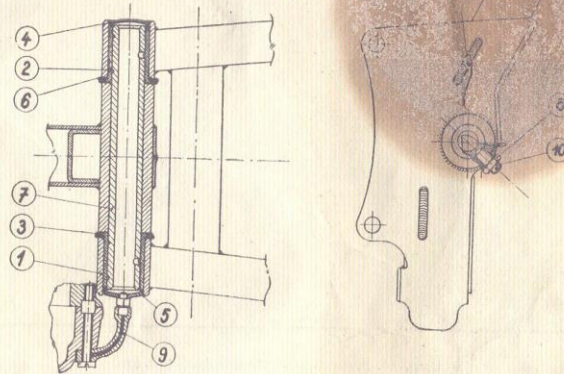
Разрез шарнира качающейся вилки нового исполнения
